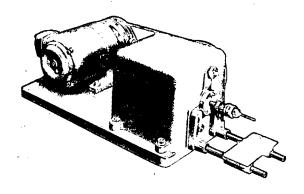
WEBA Gewindeschleifmaschine (Fritz Weern, Wuppertal-Oberbarmen)
